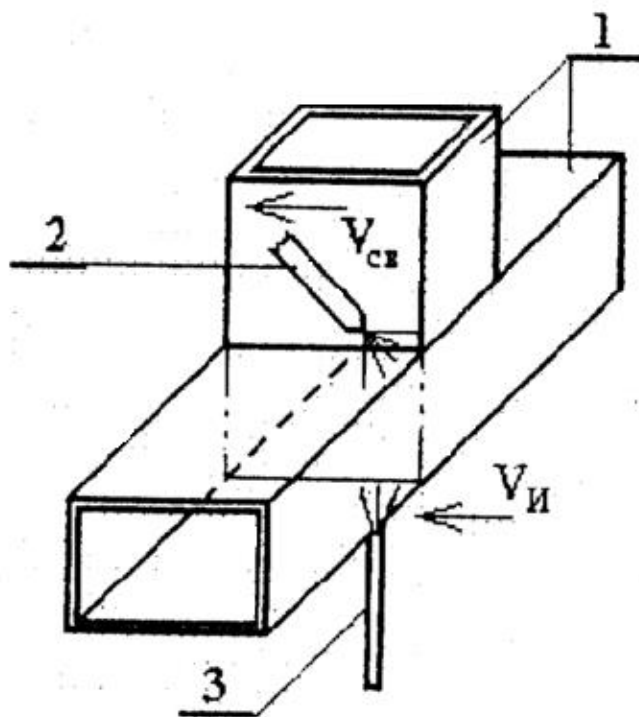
Схема сварки прямоугольных профилей с подогревом
